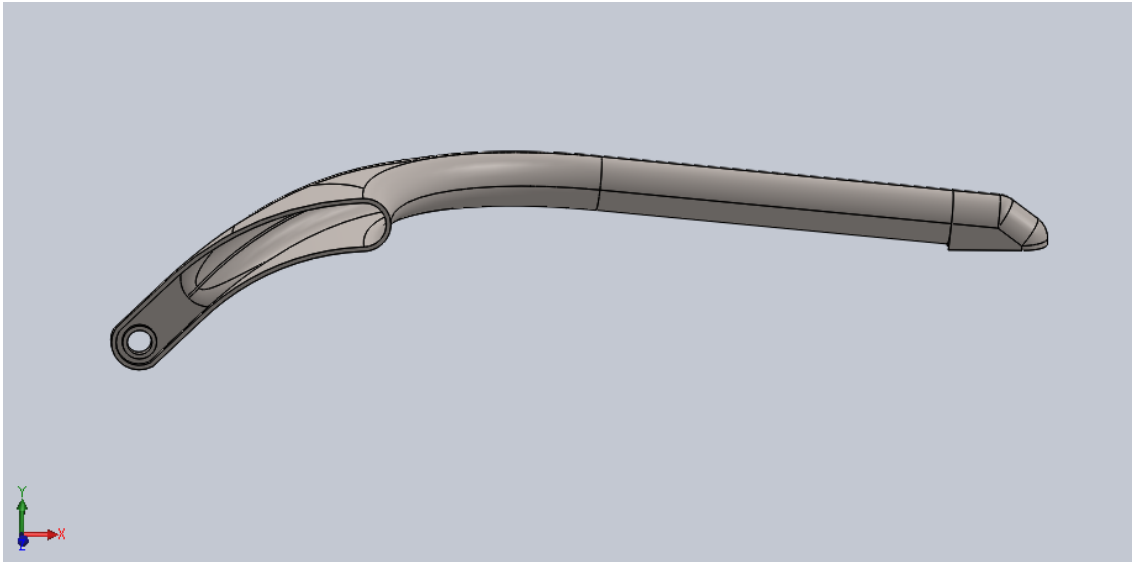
Vista de sección mostrando vaciado de la pieza.
